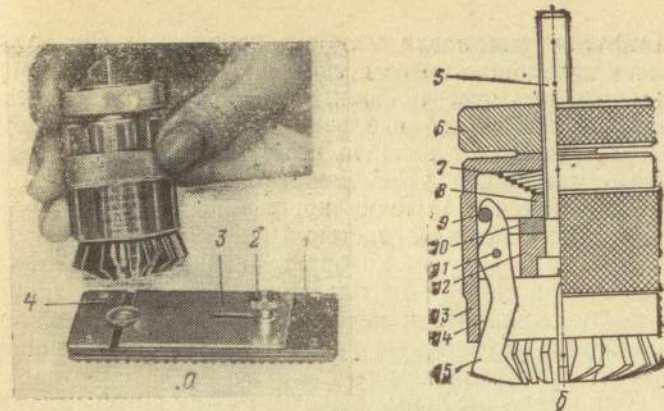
Приспособление для вставки стекол в пылевлаго-непроницаемые корпуса:
